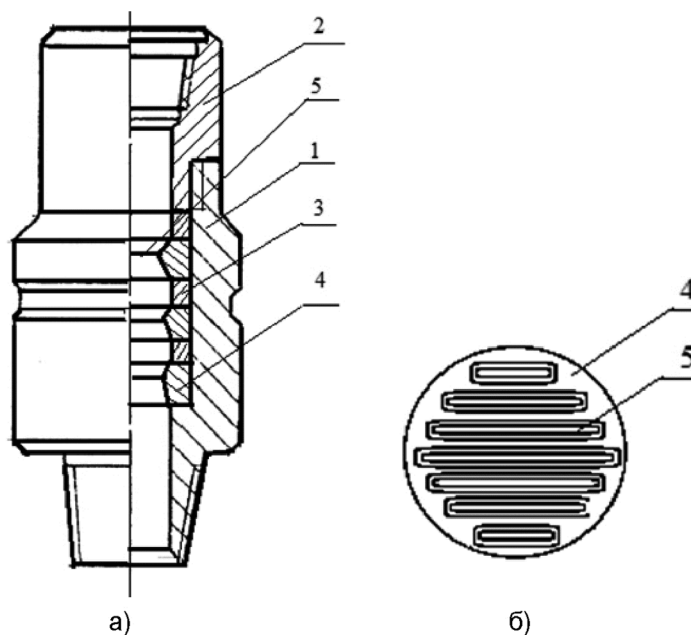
Устройство, приготавливающее быстросхватывающиеся смеси в горизонтальных скважинах:
